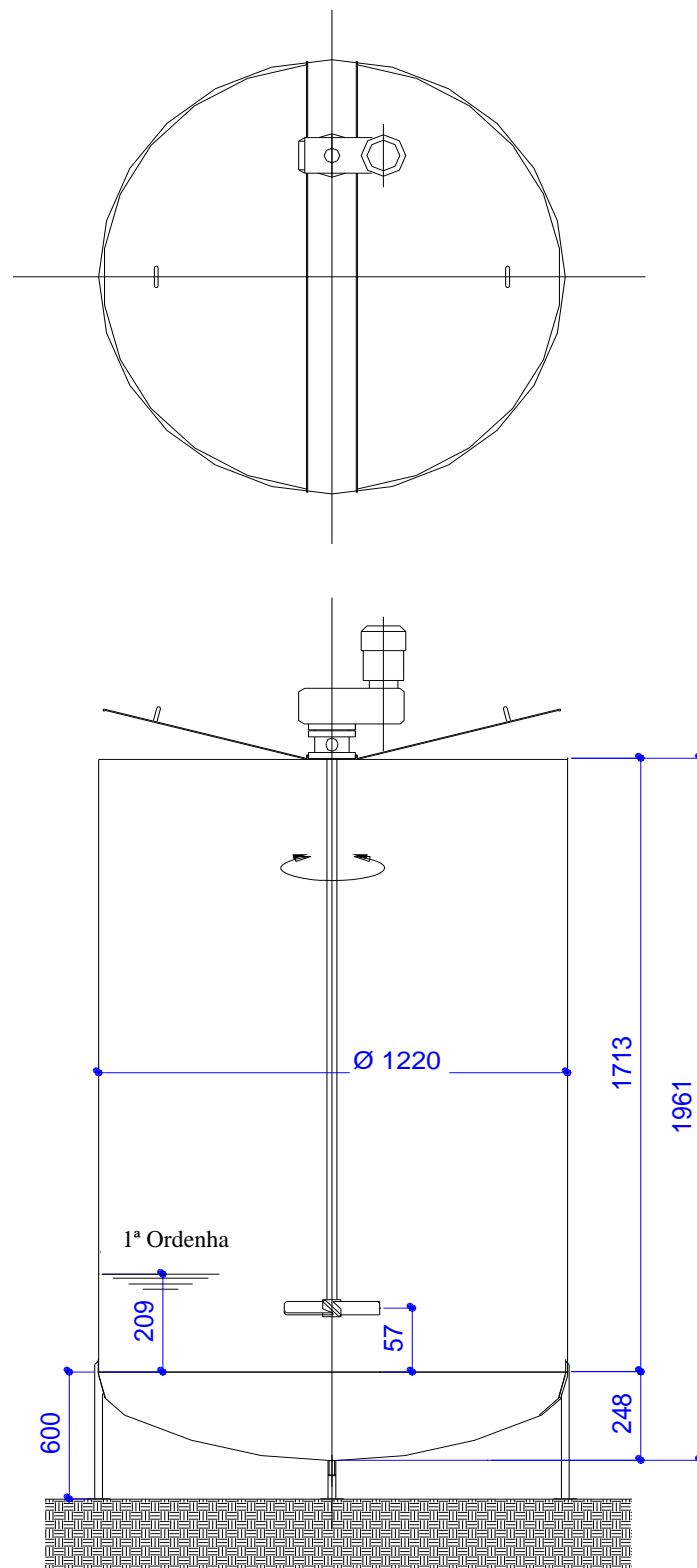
Tanque de 2000 litros (Dimensões em mm)
